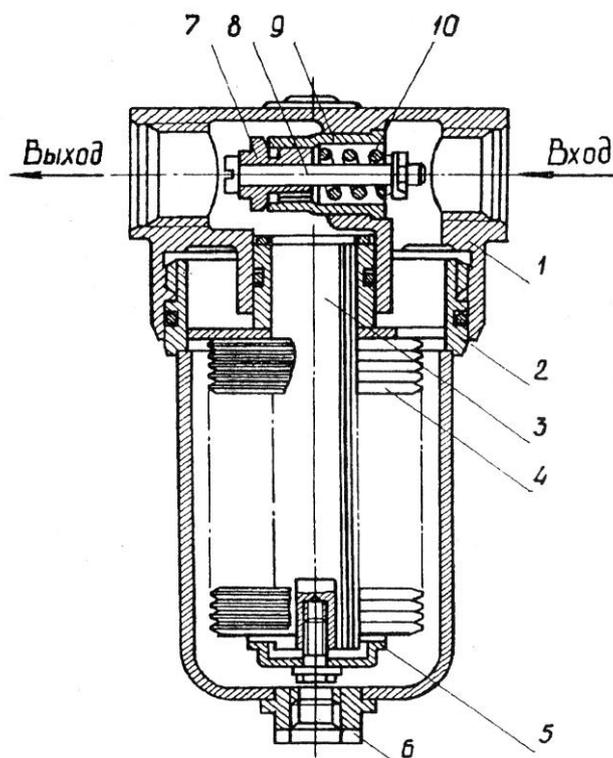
Конструкция линейного фильтра: 1 – крышка; 2 – стакан; 3 – стержень; 4 – комплект сетчатых фильтров; 5 - шайба; 6 – пробка; 7 – клапан; 8 – винт; 9 – втулка; 10 – пружина
